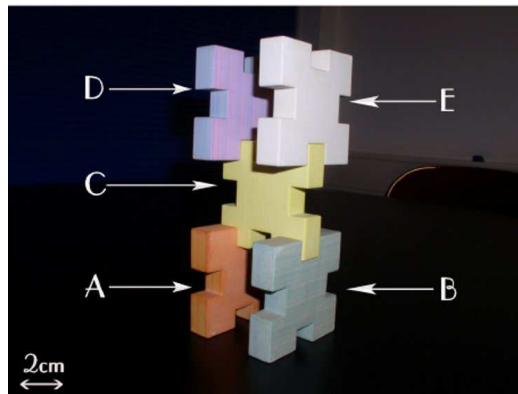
Illustration de l'assemblage 3D à réaliser.
